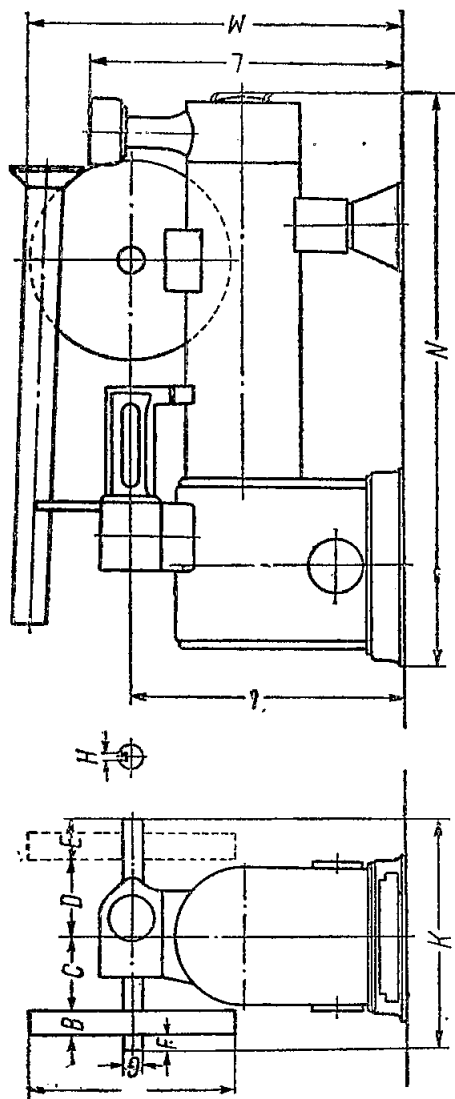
Габаритные размеры паровых локомотивов типа А и Д.
